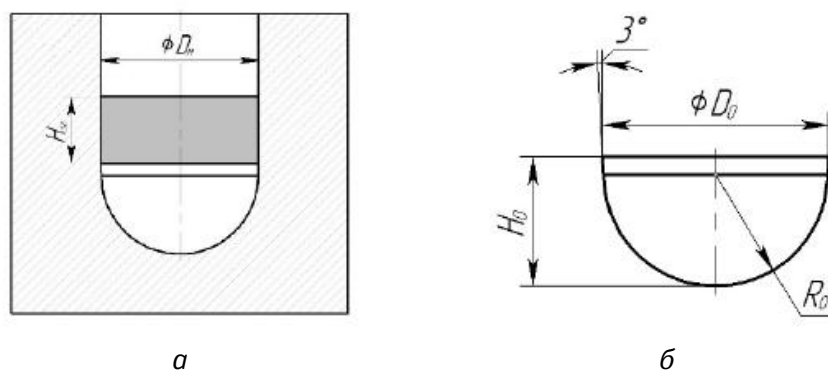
Эскиз осесимметричной штампованной заготовки со сферическим торцом [1]
